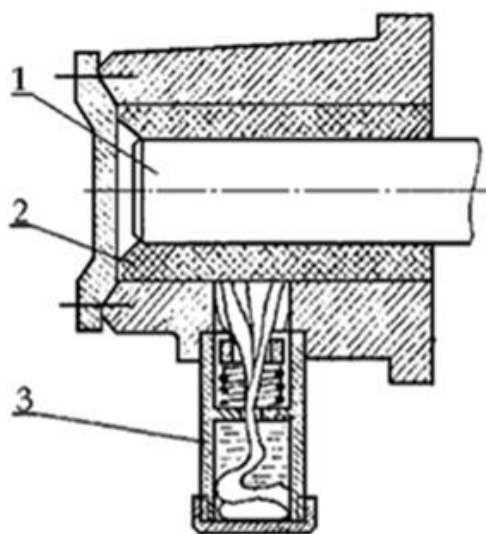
Смазывание металлокерамического подшипника при помощи фитиля:
